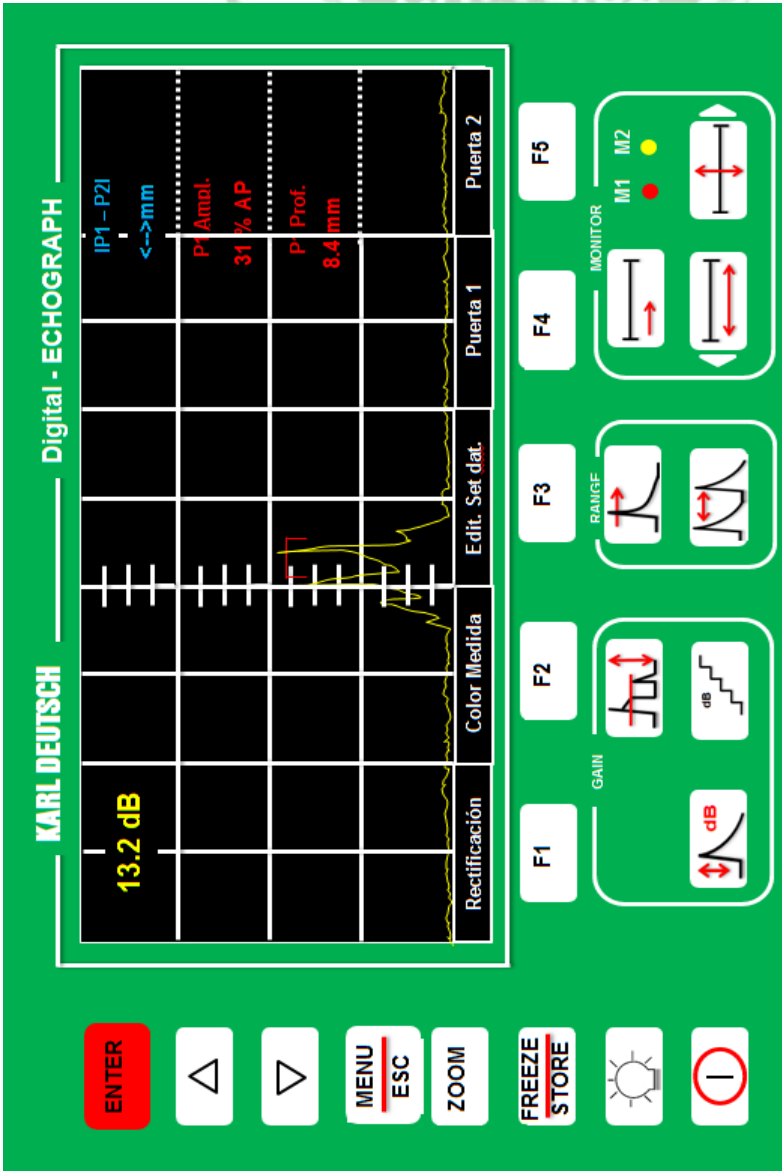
Pantalla de Inspección 1 lado izquierdo
